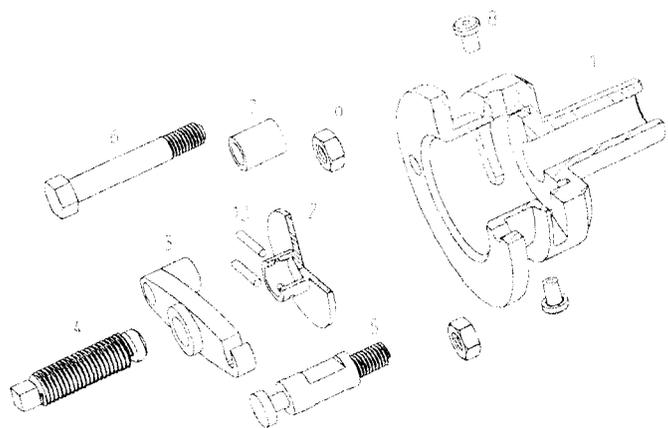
Состав сборочной единицы: 1 - корпус, 2 - тарелка, 3 - планка, 4 - винт, 5 - стойка, 6 - болт, 7 - втулка, 8 - втулка кондукторная, 9 - гайка, 10 - штифт
